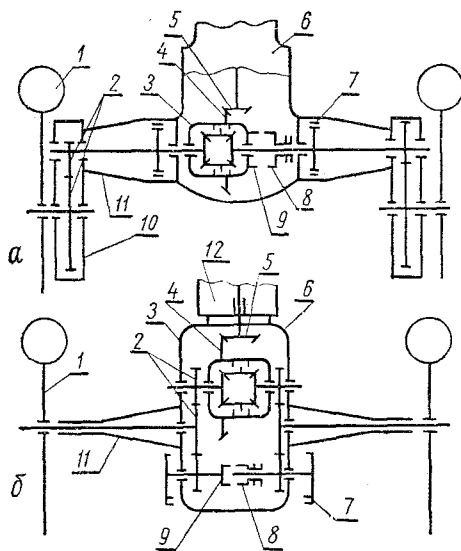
Схемы силовой передачи колесных универсально-пропашных тракторов: 1 — ведущее колесо; 2 — шестерни конечной передачи; 3 — дифференциал; 4 — ведомая шестерня главной передачи; 5 — ведущая шестерня главной передачи; 6 — корпус заднего моста; 7 — тормоз; 8 — подвижная полумуфта механизма блокировки; 9 — неподвижная полумуфта механизма блокировки; 10 — картер конечных передач; 11 — рукав полуоси; 12 — коробка передач.
